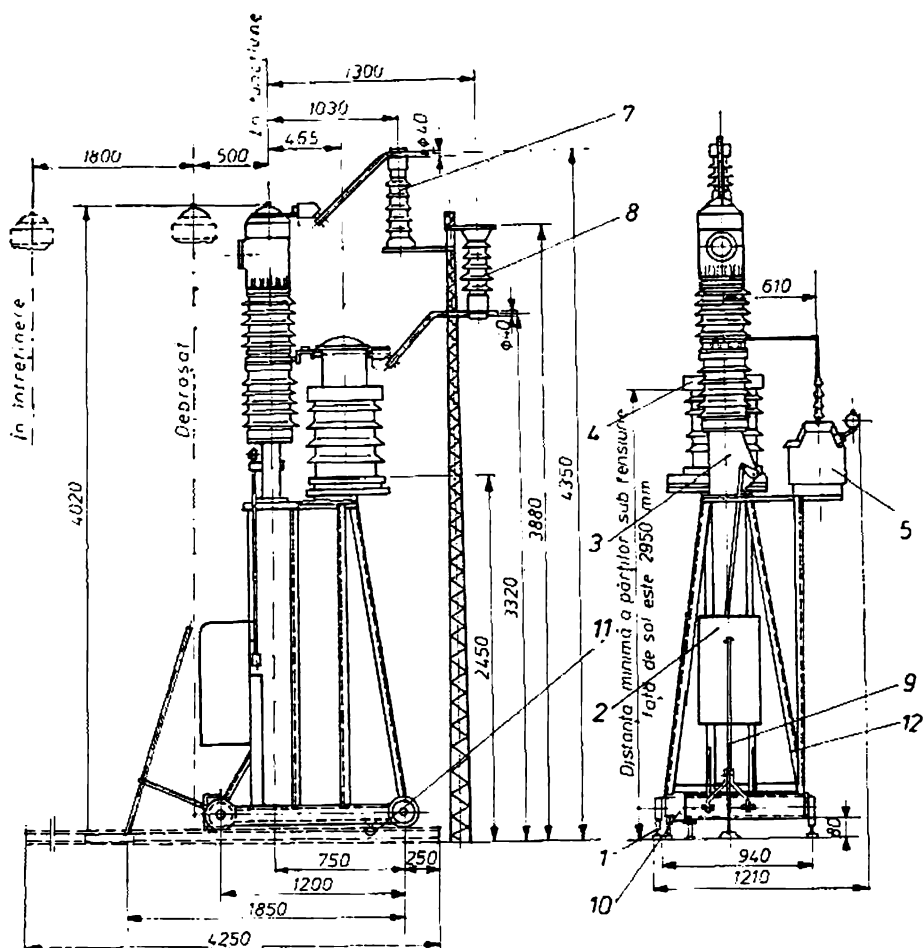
Înteruptoare IUP-25/1250 cu CESU 35/600, 1000 și TEBU 25/0,1. Dimensiuni de gabarit:
